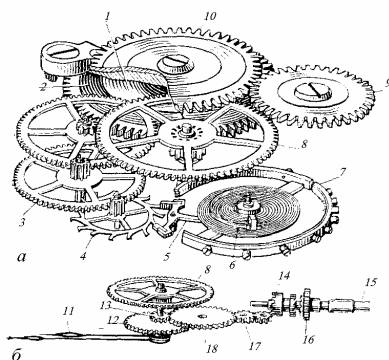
Механизм наручных часов (а) и стрелочный механизм (б): 1 – заводной барабан; 2 – пружина; 3 – секундное колесо; 4 – спусковое колесо; 5 – анкерная вилка; 6 – концевая кривая; 7 – баланс; 8 – центральное колесо; 9 – заводное колесо; 10 – барабанное колесо; 11 – часовая стрелка; 12 – часовое
